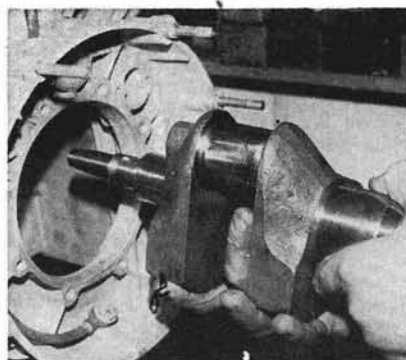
Dépose du vilebrequin (Photo RMT)
